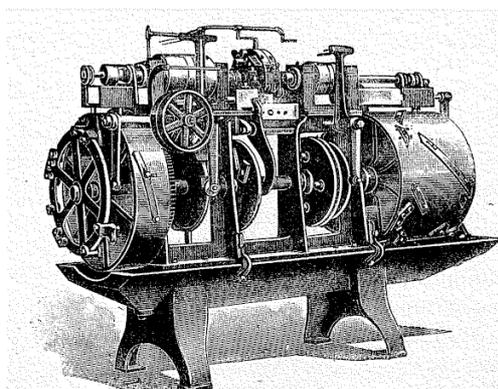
Machine à vis *Spencer* à double revolver, construite par la *Spencer Machine Screw Co*, Hartford.
